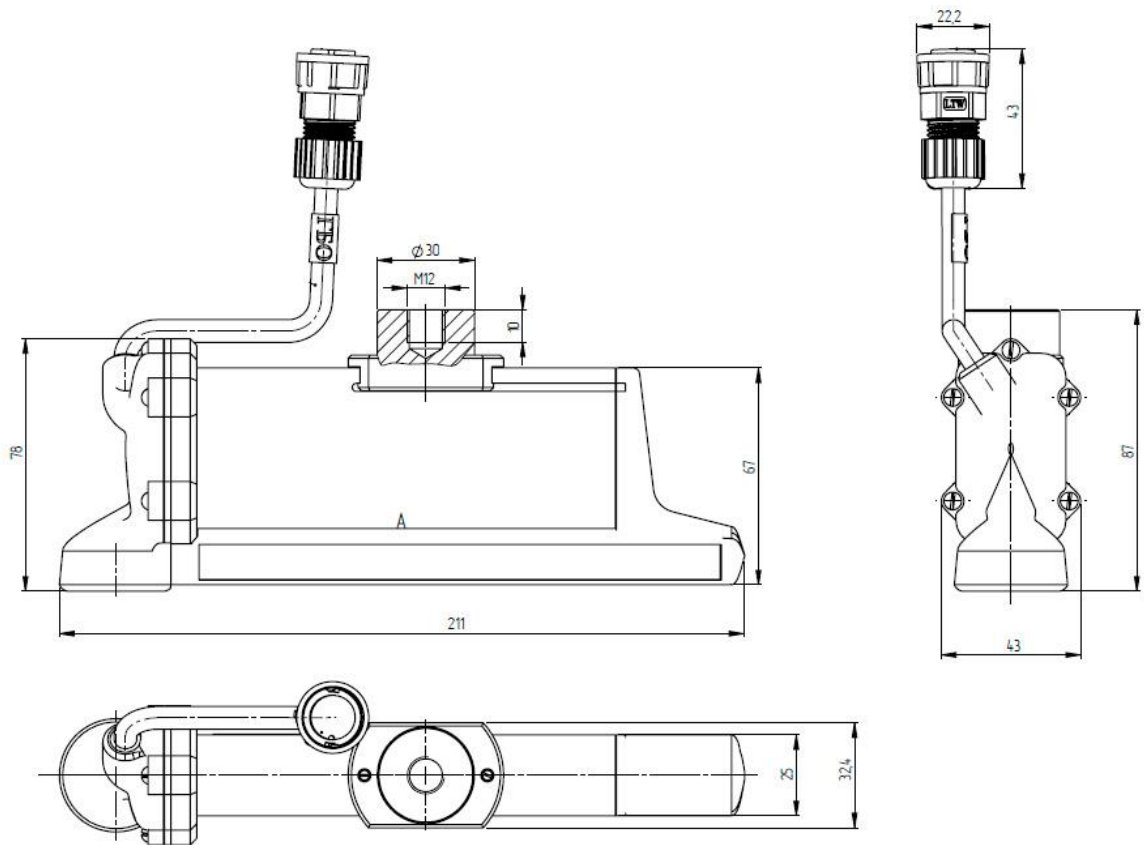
Габаритный чертеж моноблока (кронштейн для крепления к штанге из набора КИТ006)
